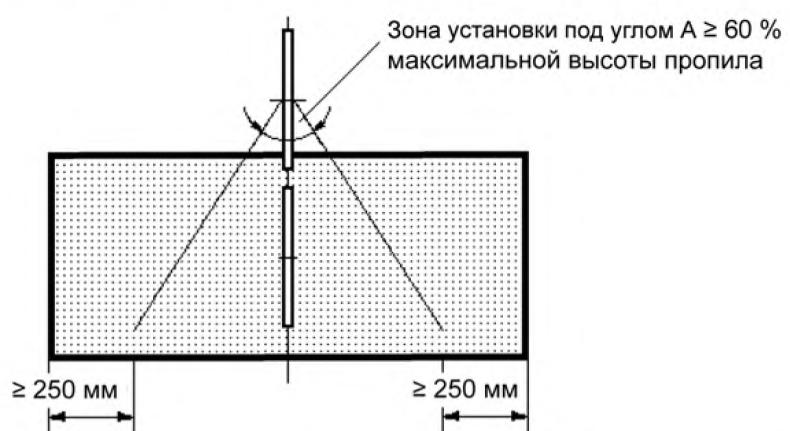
а) – Опорная поверхность для обрабатываемой заготовки в станках-автоматах
